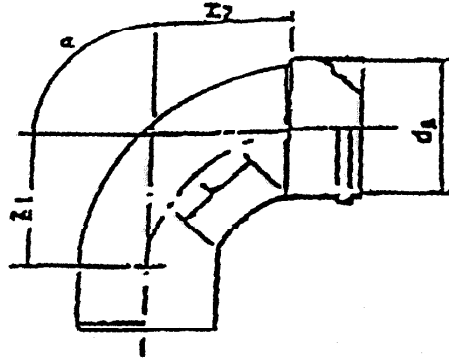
Beispielhafte Ausführung einer elastomeren Dichtringverbindung mit in der Muffe angeordnetem Dichtring
